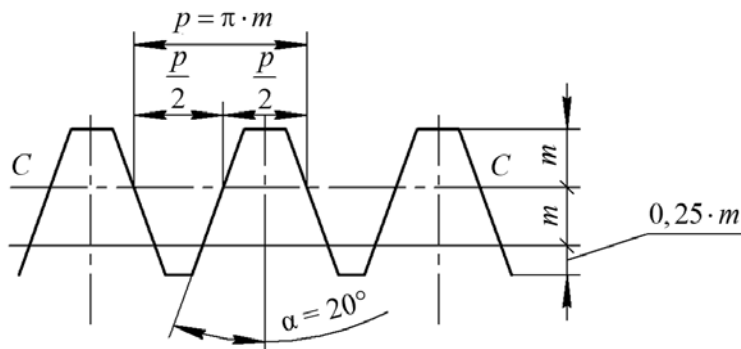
Основные параметры профиля зуба зубчатой рейки
